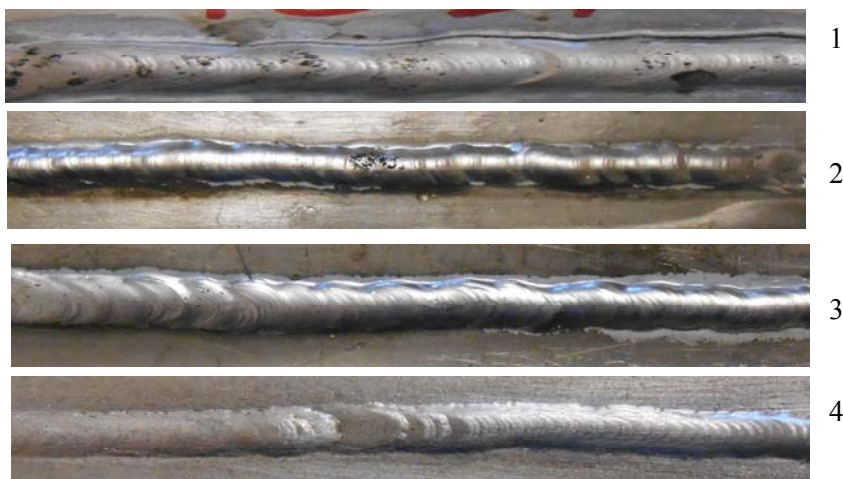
Фрагменты валиков на тонколистовых металлоконструкциях, наплавленных полуавтоматом и автоматом: 1 – валик, полученный при сварке с управляемой импульсной подачей электродной проволоки; 2, 3 (стыковой шов) 4 (автоматический режим) – валики, полученные при дозированной подаче электродной проволоки
